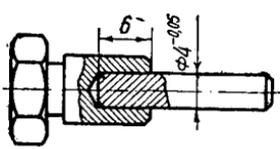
Латунная ось рычага поплавка для керосина с головкой, изготовленной из стали
